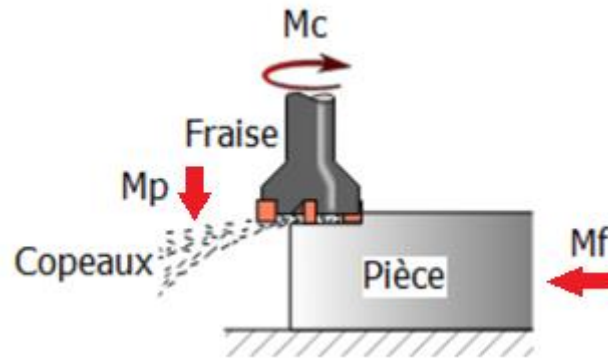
Mouvements relatifs entre l'outil et la pièce à usiner.
